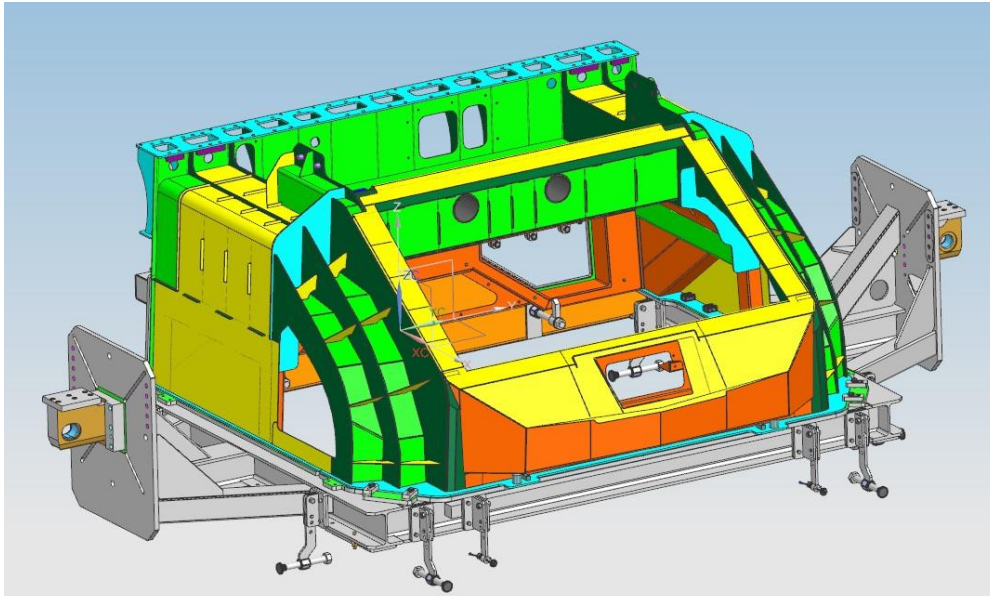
Utillaje preparado para la fase de soldadura con los conjuntos aprietes descolgados.
